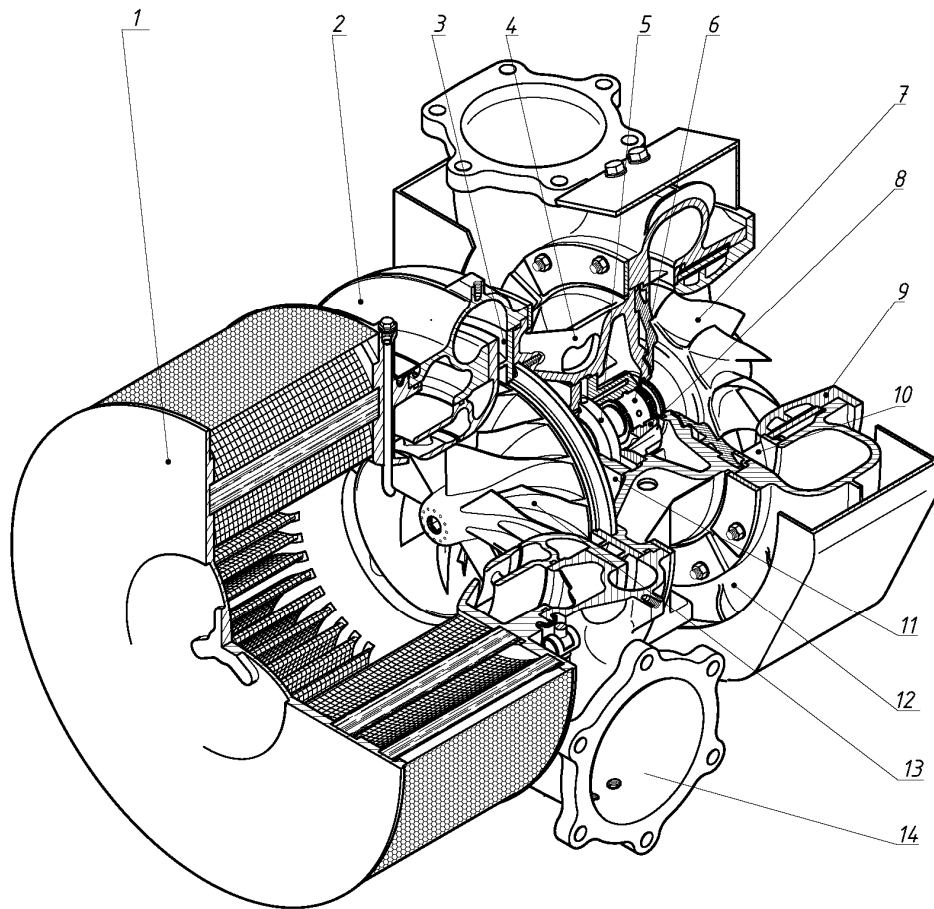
Турбокомпресор з радіальної турбіною: 1 – повітряний фільтр; 2 – вихідний патрубок компресора; 3 – дифузор, 4 – корпус підшипникового вузла; 5 – осьовий підшипник; 6 – радіальний підшипник зі сторони турбінного колеса; 7 – турбінне колесо; 8 – підшипниковий вузол; 9 – дефлектор турбіни; 10 – направляючий апарат турбіни; 11 – ущільнення з боку компресора; 12 – вихідний патрубок турбіни; 13 – колесо компресора
